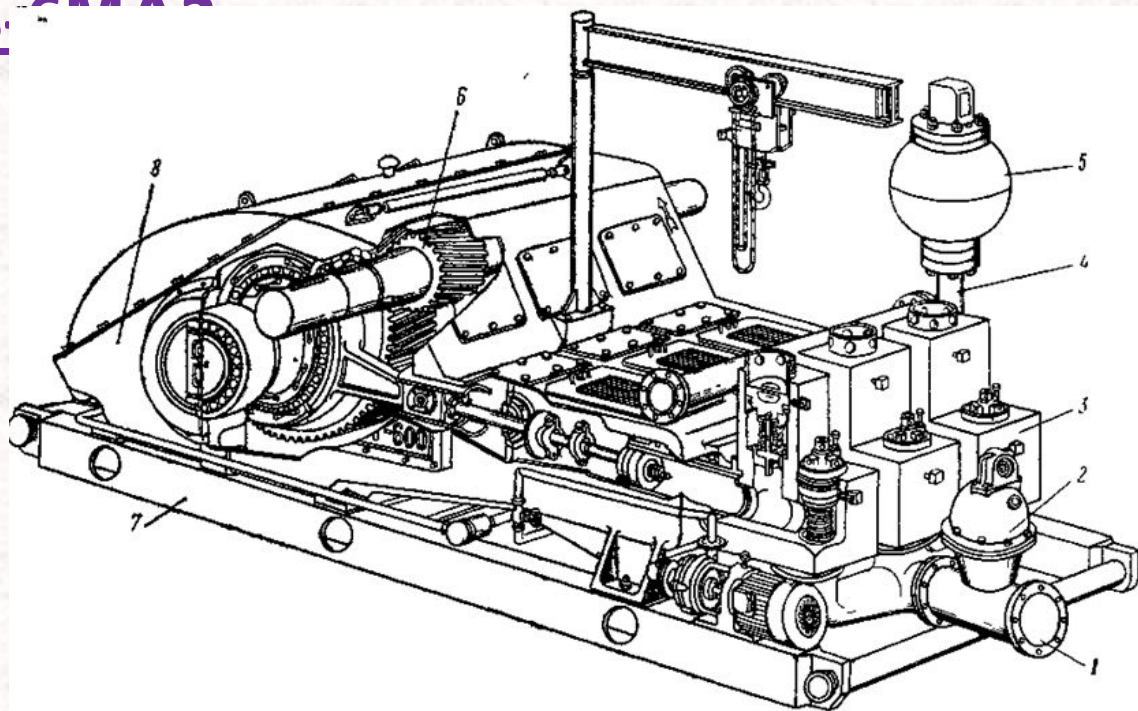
Общий вид насоса (1 – всасывающий коллектор; 2 – всасывающий компенсатор-колпак; 3 – гидравлическая коробка; 4 – нагнетательный коллектор; 5 – компенсатор высокого давления; 6 – трансмиссионный вал; 7 – рама-салазка)
